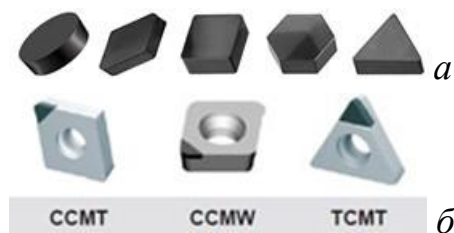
PCBN- (а) і PCD-пластини (б) для різального інструменту.
